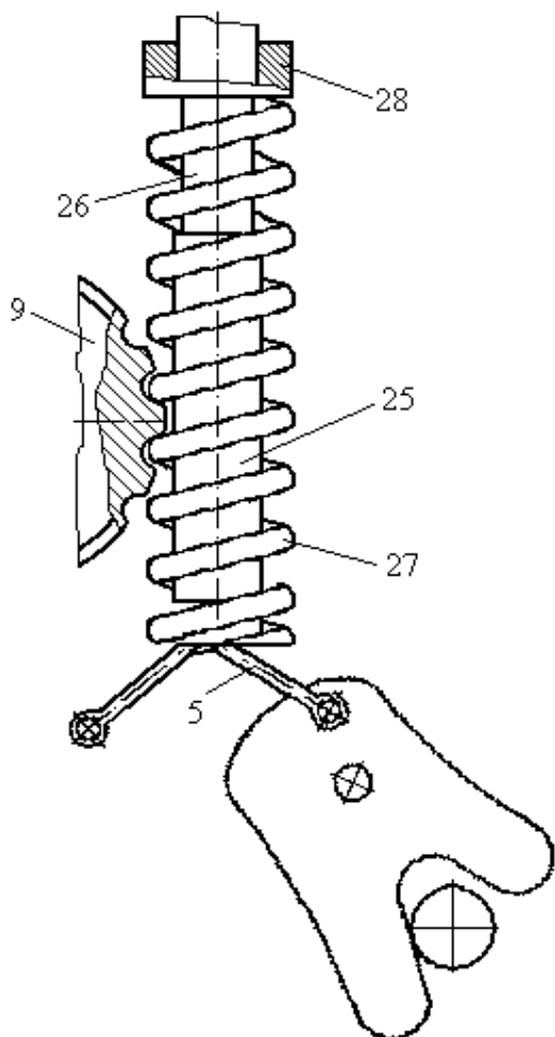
Привод защелки с червяком в виде вала с охватывающей его пружиной
